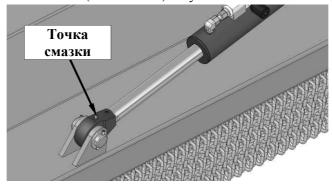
Место смазки шарнира гидродвигателя (смазка STP)
